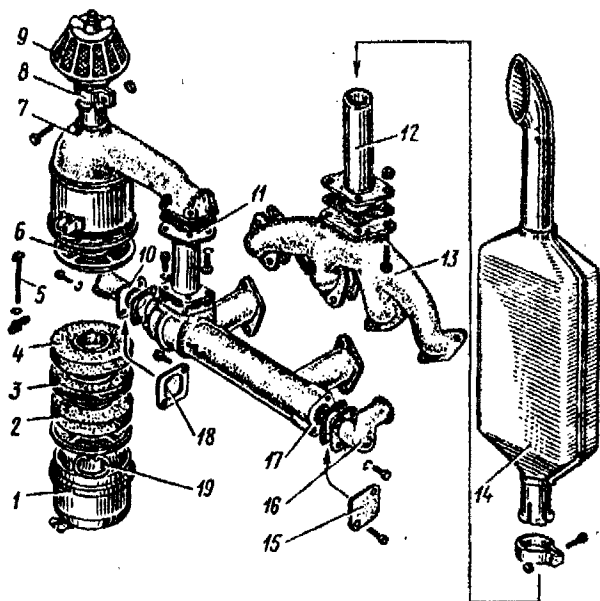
Детали воздухоочистителя, впускного и выпускного коллекторов (Д-65): 1 – поддон воздухоочистителя; 2 – нижний фильтрующий элемент; 3 – средний фильтрующий элемент; 4 – верхний фильтрующий элемент; 5 – стяжной болт; 6 – сетка; 7 – корпус; 8 – хомут; 9 – фильтр грубой очистки воздуха; 10 – выпускной патрубок пускового двигателя; 11 – переходной патрубок; 12 – выпускной патрубок; 13 – выпускной коллектор; 14 – глушитель; 15, 18 – заглушки; 16 – патрубок; 17 – впускной коллектор; 19 – разжимное кольцо
